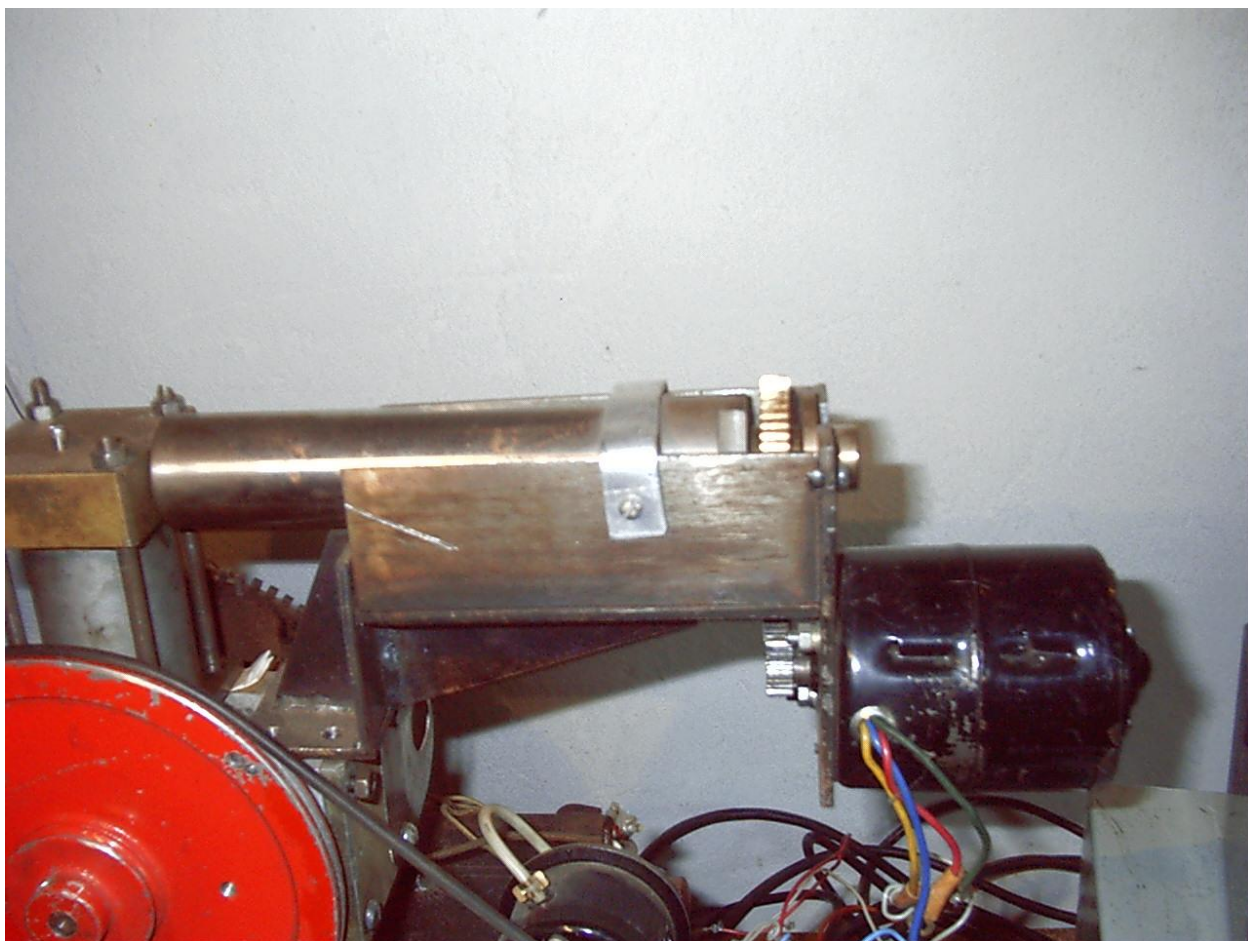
Общий вид дополнительного цилиндра с электродвигателем
